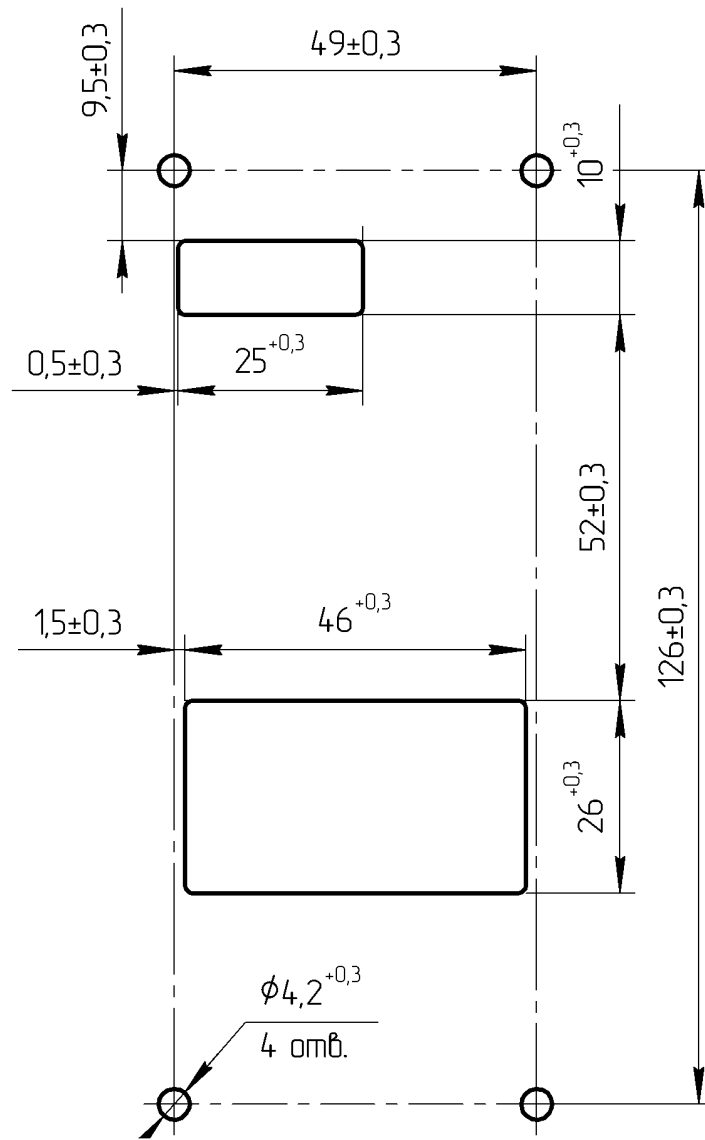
Разметка отверстий для монтажа индикатора выносного тип 2
